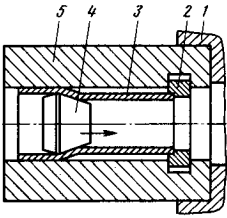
Обработка с размещением детали в жестком корпусе: 1 — опорная плита станка; 2 — раздвижная опора; 3 — деталь; 4 — инструмент; 5 — жесткий корпус
